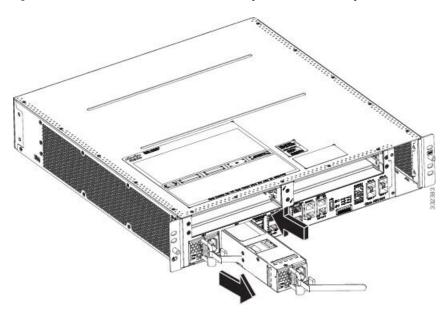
Remover ou instalar um módulo de alimentação AC ou DC (alimentação AC do Cisco ASR 9001 apresentada)
